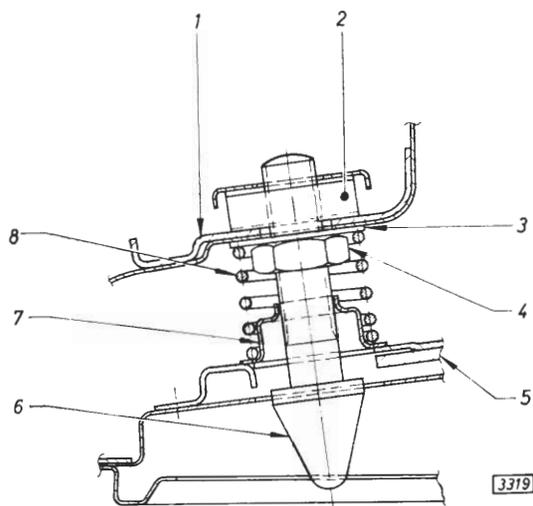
Befestigung des Führungzapfens an Motorhaube
